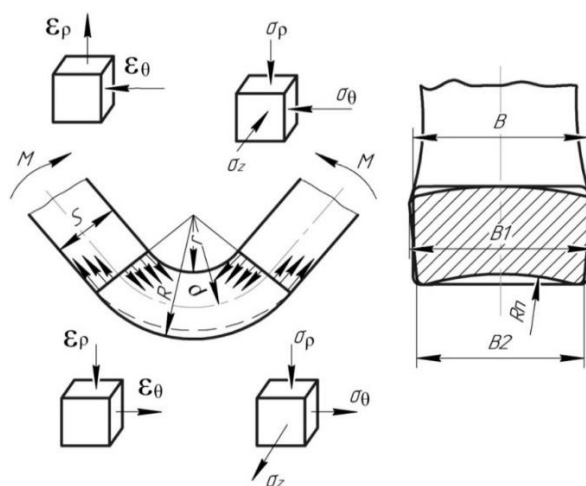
Искажение формы заготовки при изгибе прямоугольной заготовки моментом
